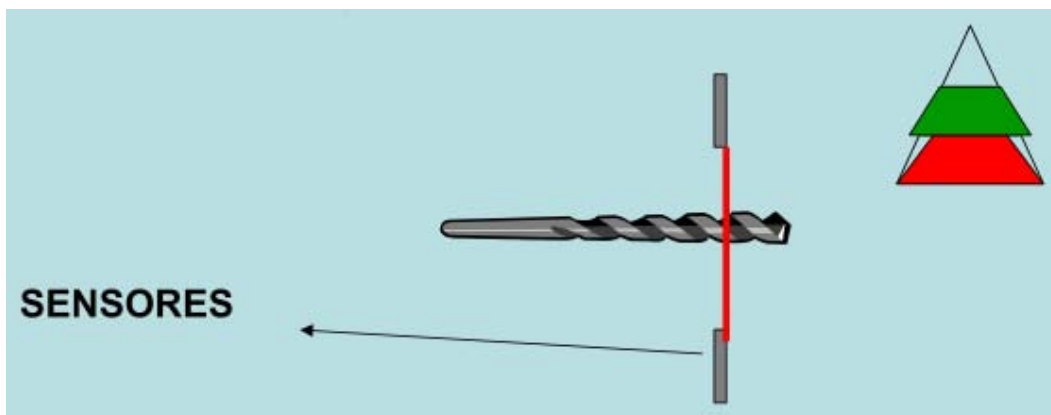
Sensores en la manufactura de un Monoblock.
